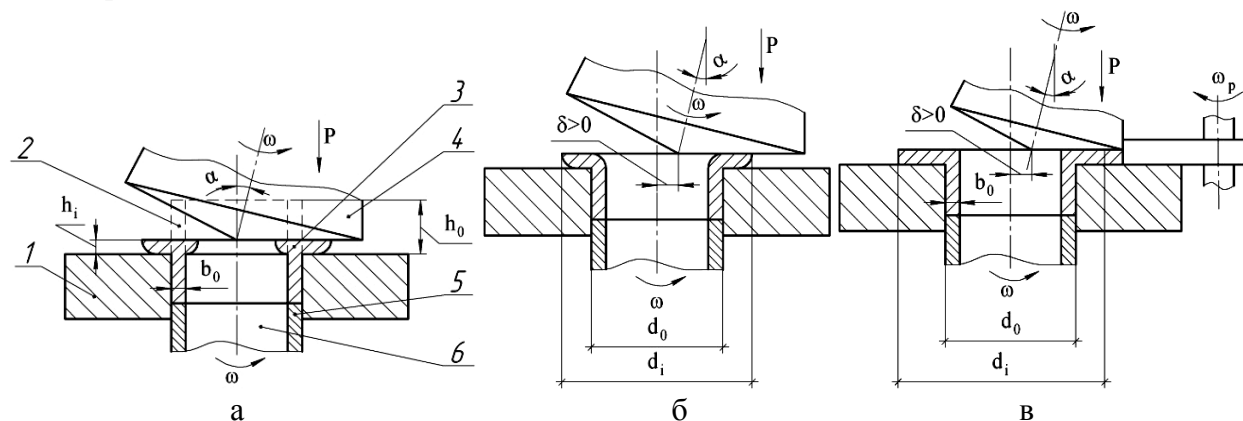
Схемы высадки раскаткой буртов (1 – матрица; 2 – заготовка; 3 – изделие; 4 – валок; 5 – выталкиватель; 6 – оправка):
